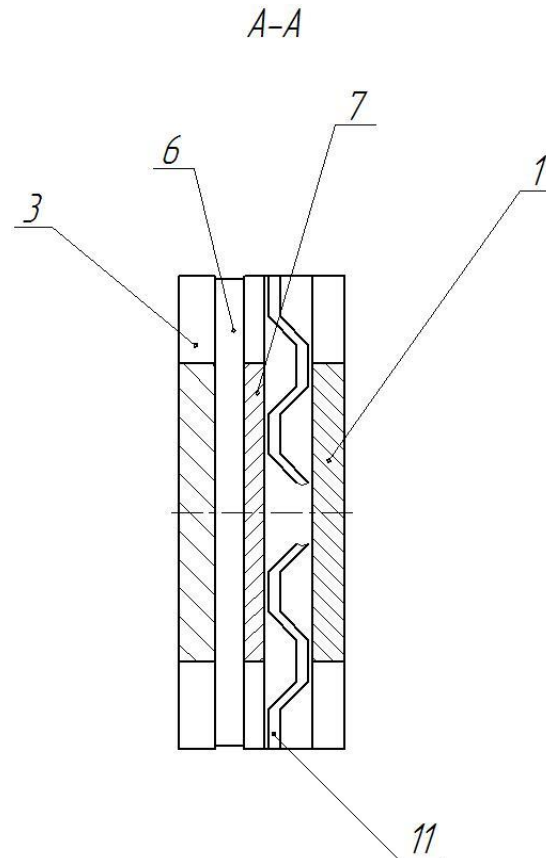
Розпилювальний пристрій з гасінням коливань, переріз А-А.
